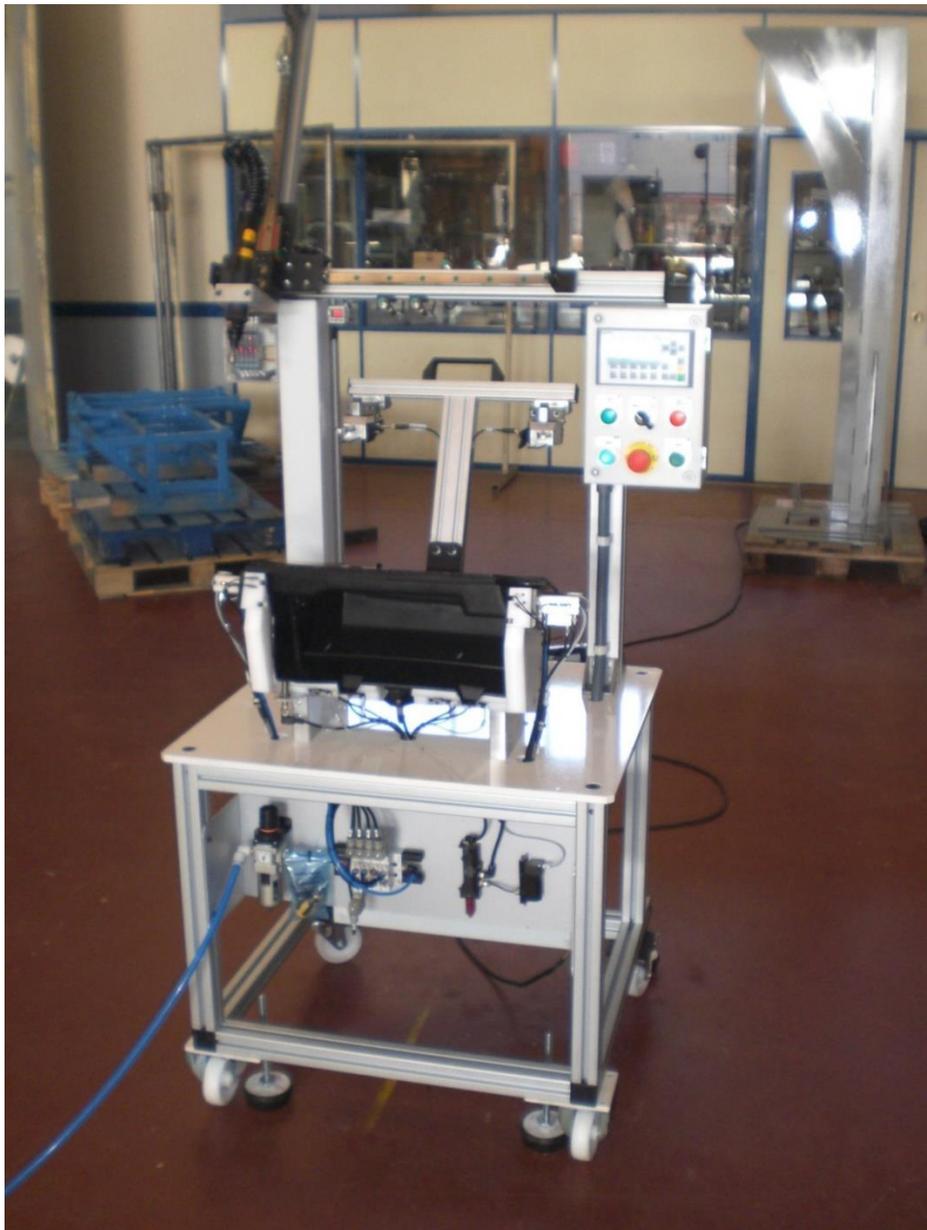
Máquina terminada, PUESTO DE MONTAJE DE GUANTERA FORD MOD. CD539
